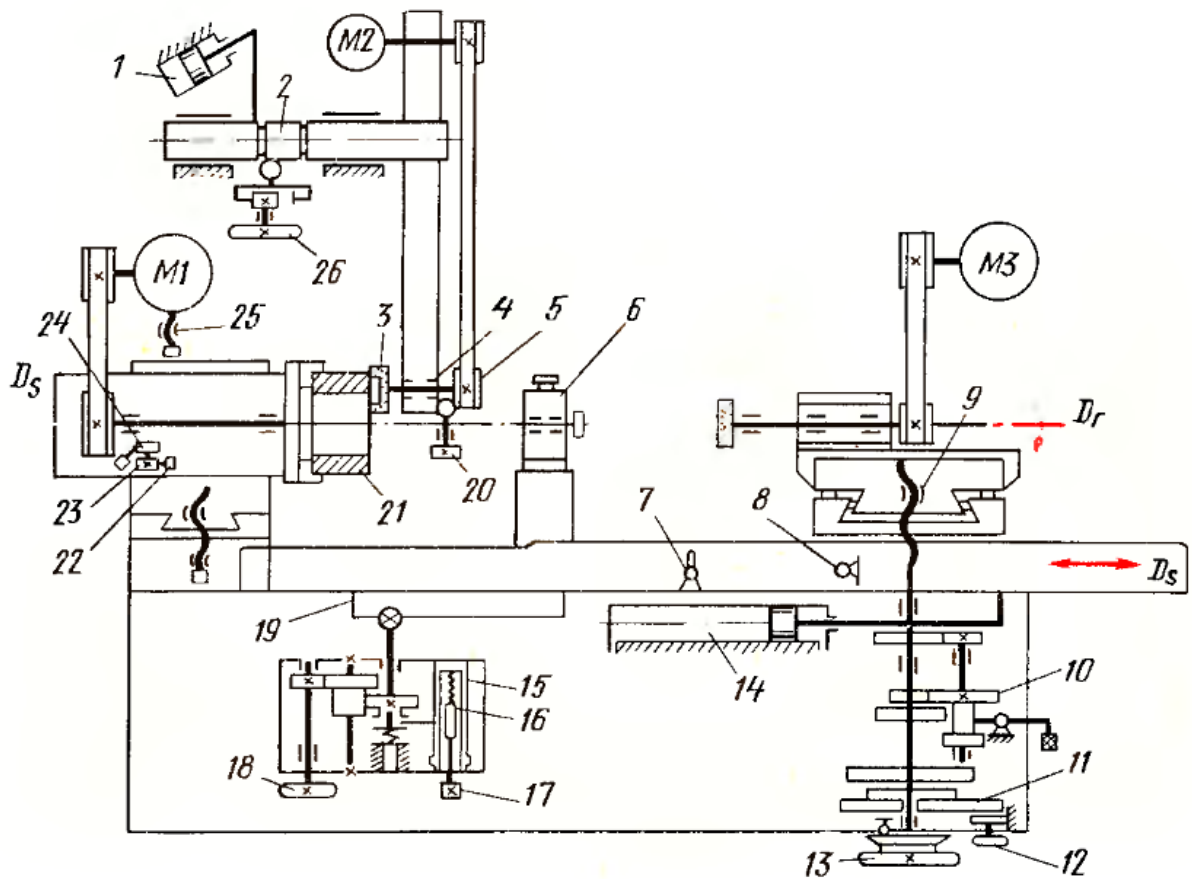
Кинематическая схема внутришлифовального станка мод. 3K227B
